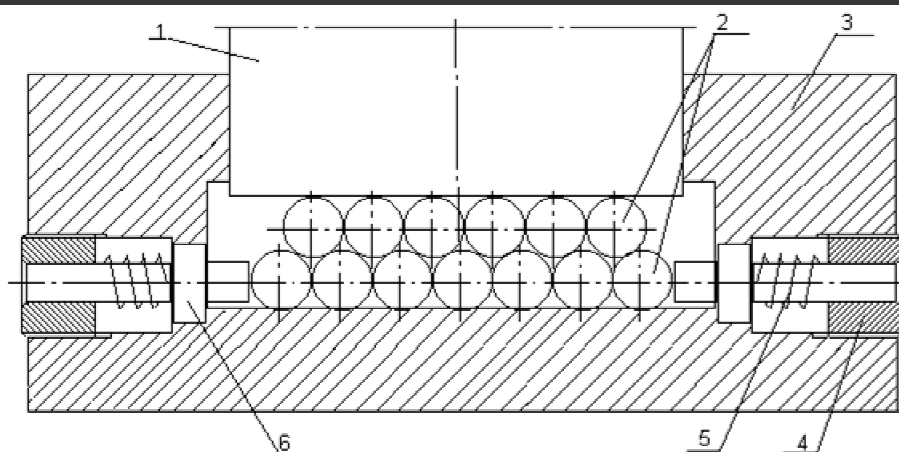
Схема буферного устройства пружинно-шарикового типа
